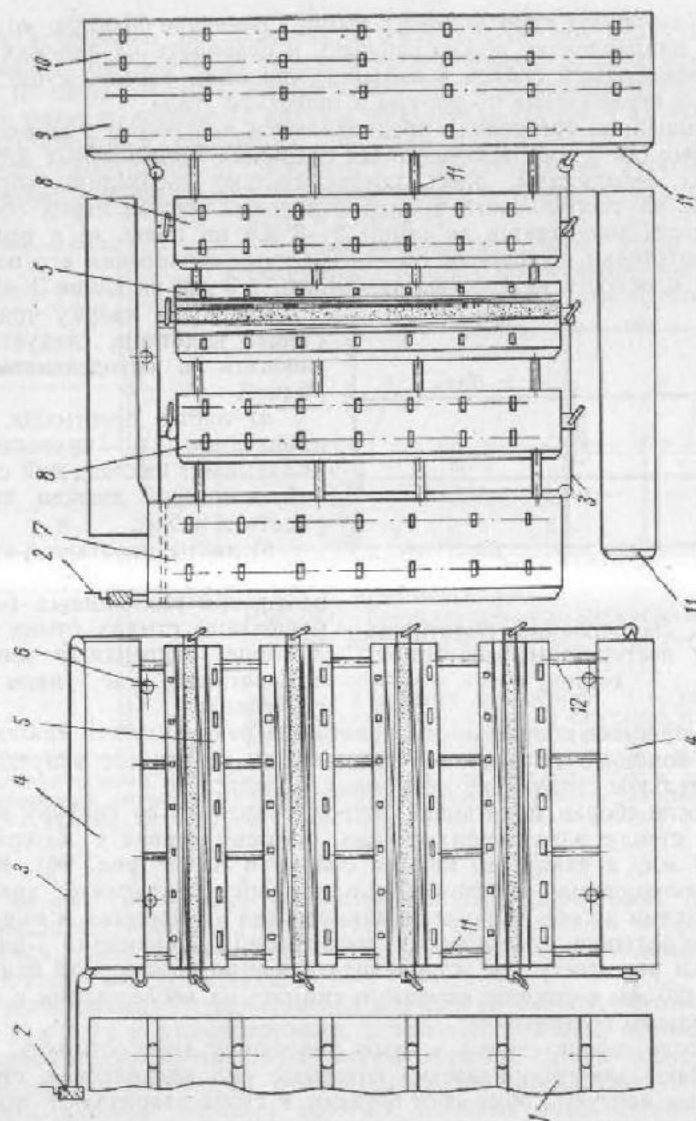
Магнитный стенд для автоматической сварки полотнищ.
